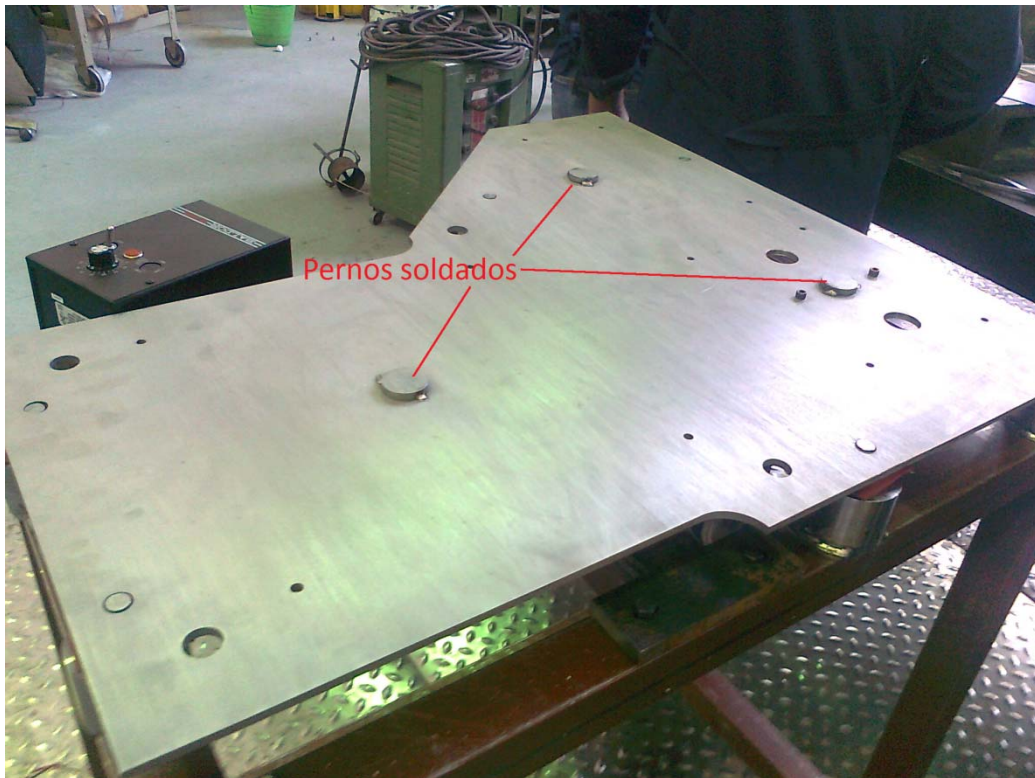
Primer paso del ensamble del sistema (soldado de pernos a la base del sistema).
